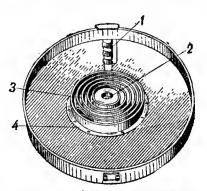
Нижний диск магазина: 1 — лоток, 2 — втулка, 3 — ваводная пружина, 4 — обруч
